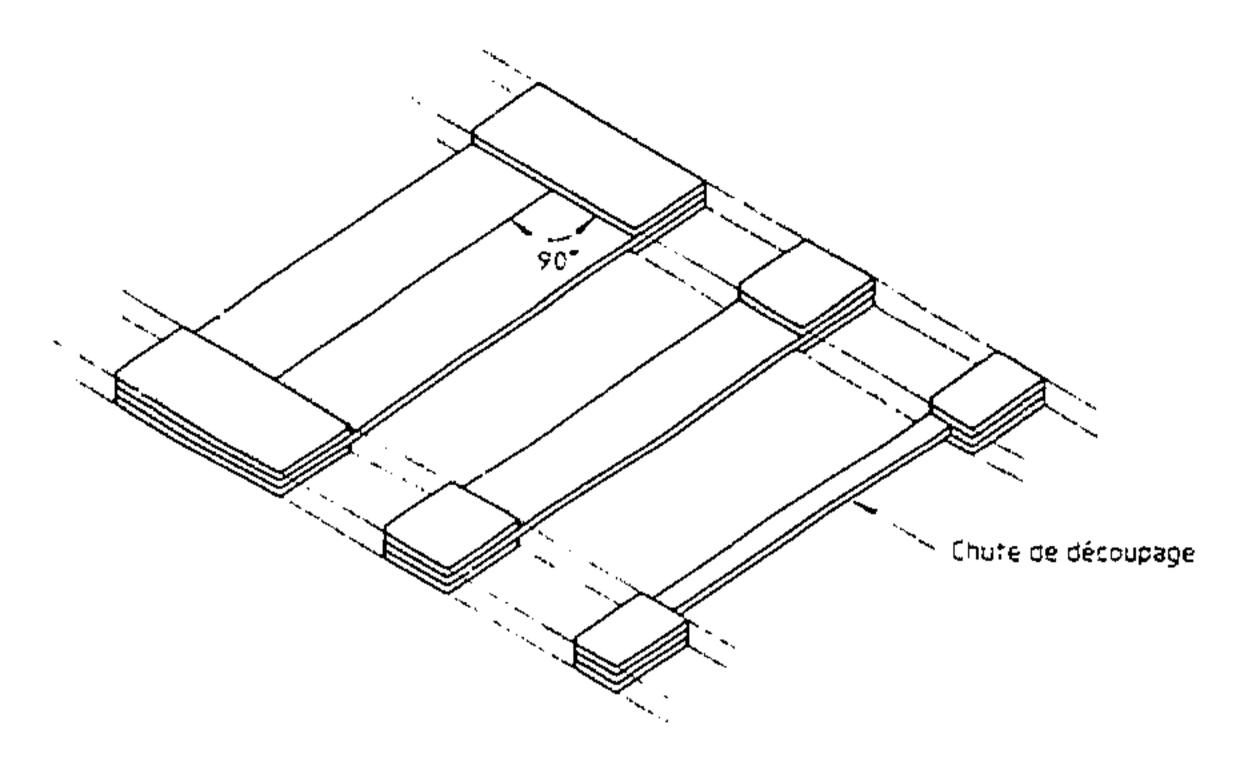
Panneau équipé de talons pour la préparation des éprouvettes
